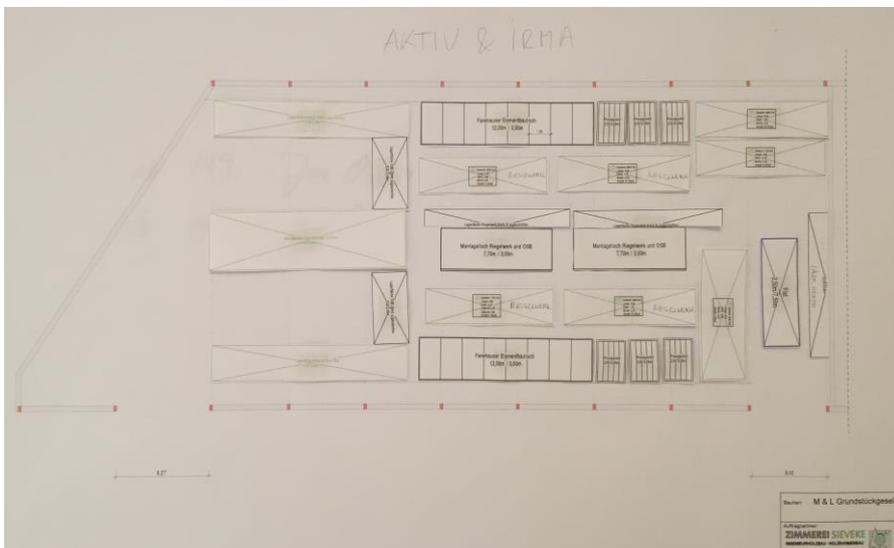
Entwurf Halleneinrichtungsplan (Projekt B)⁴³¹
